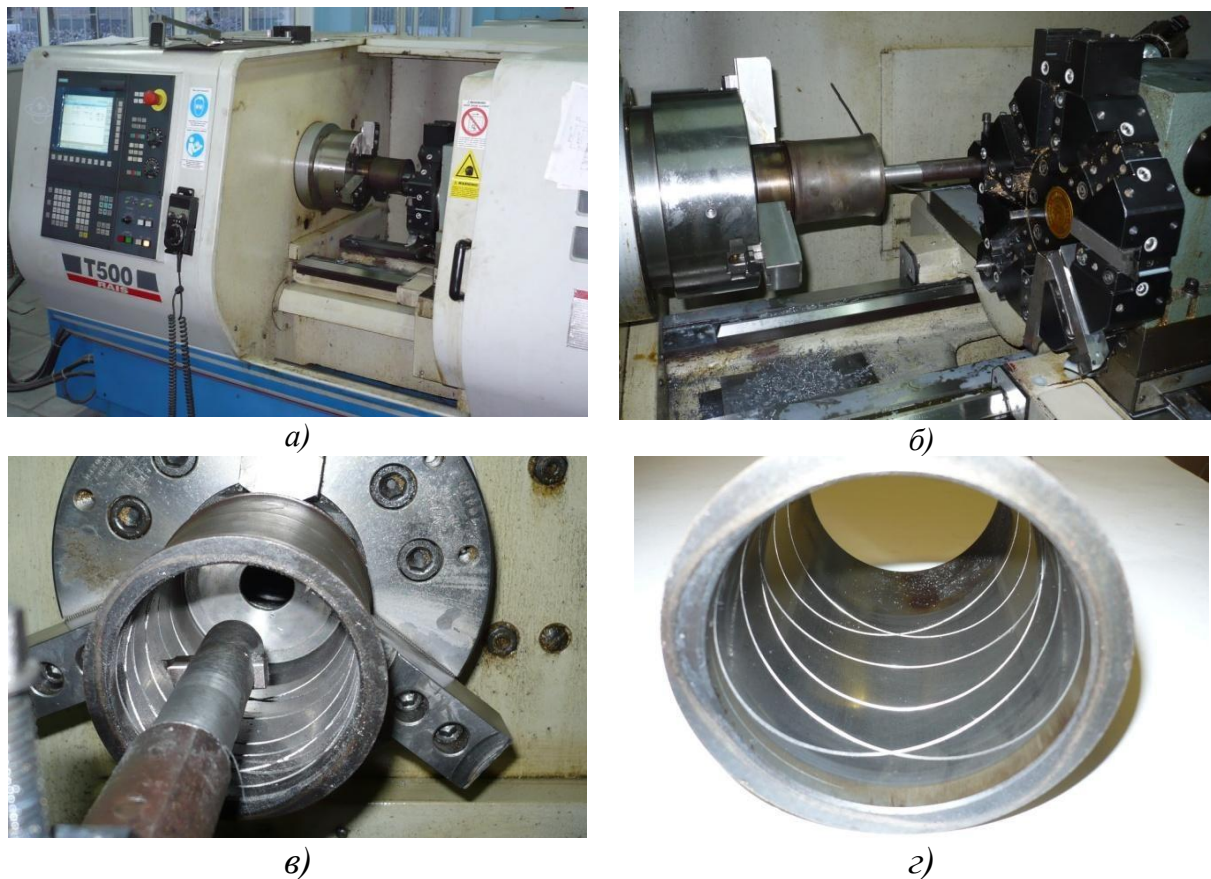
Нарізування кільцевих канавок: а) загальний вигляд центровочно-токарного верстата Т-500; б) трикулачковий патрон; в)різець ВК8; г)гільза з кільцевими канавками
